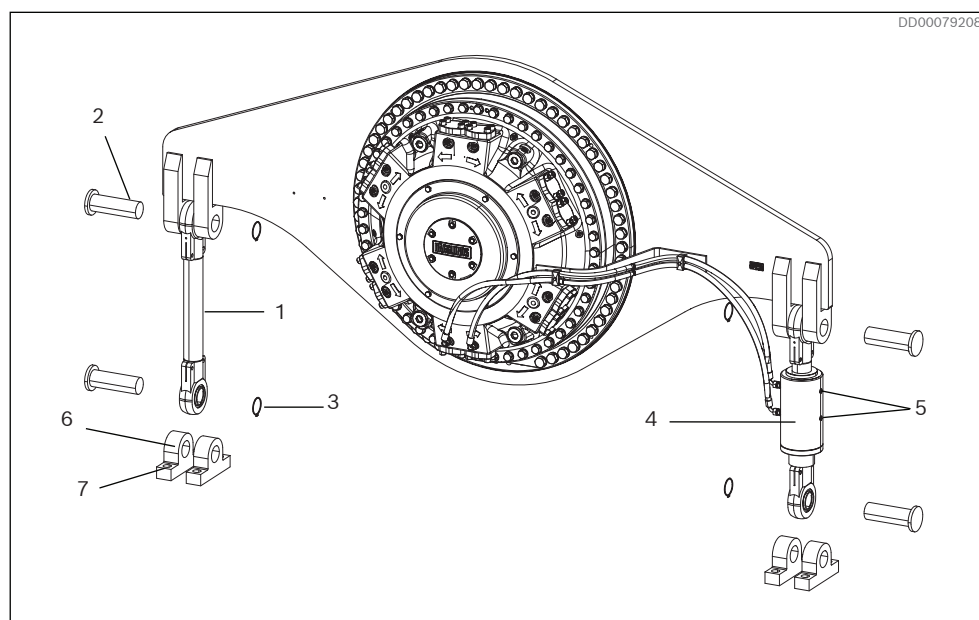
Шарнирное соединение и гидравлический цилиндр для DTCBM 1600 – DTCBM 4000
